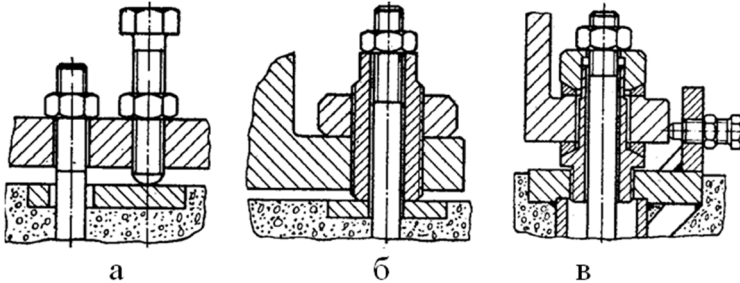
Конструкції гвинтових опор та верстатів, які закріплюються болтами
